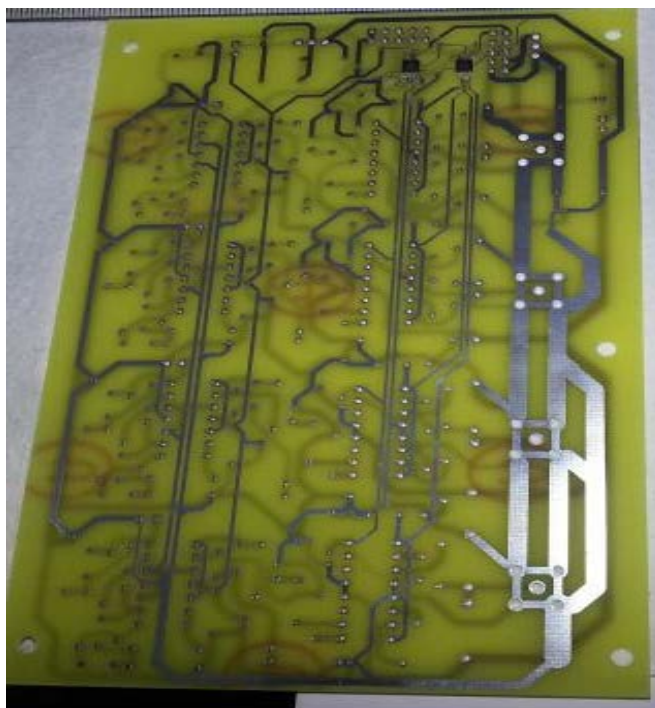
Placa antes de realiza el soldado de los componentes
